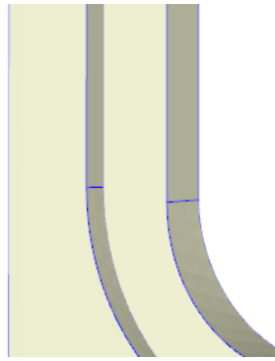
RUN 4 - Linha de soldadura não ilustrada
